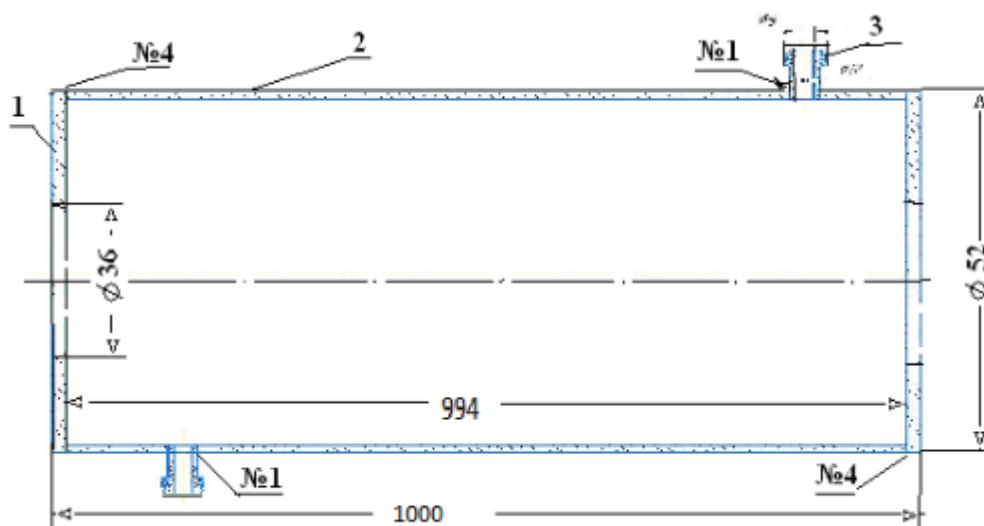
Конструкция трубопровода с подогревом в разрезе
